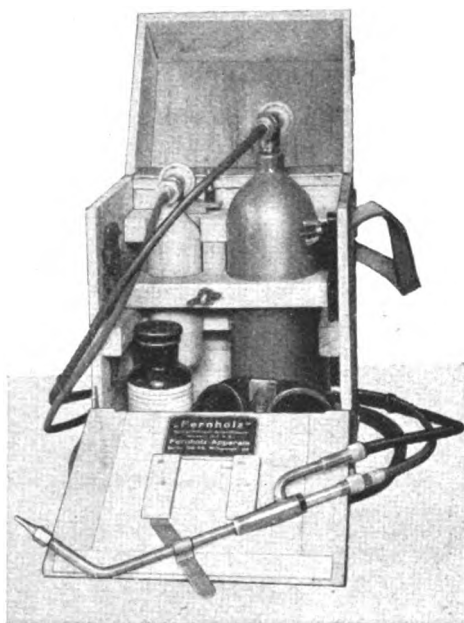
Montagegerät zur Autogenschweißung von Starkstromkabeln.
